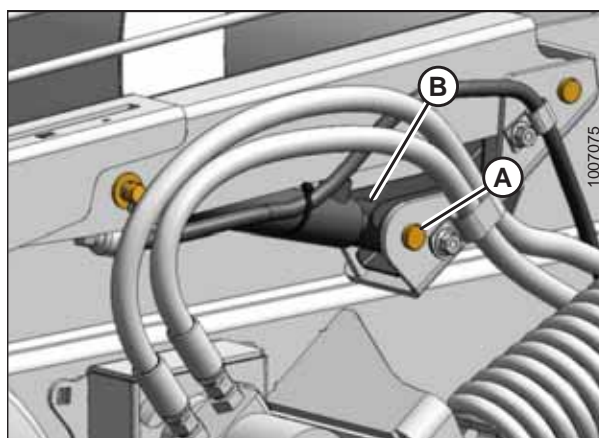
Главный гидроцилиндр — Левая сторона жатки
